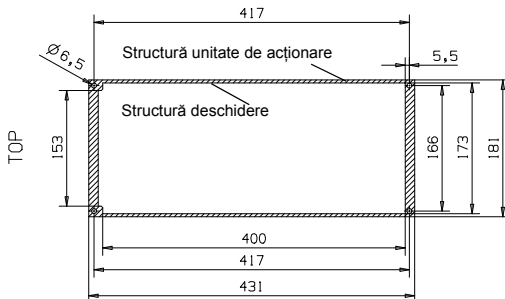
Dimensiuni de decupare la montarea cu flanșă pentru MI5 (Unitate: mm)
